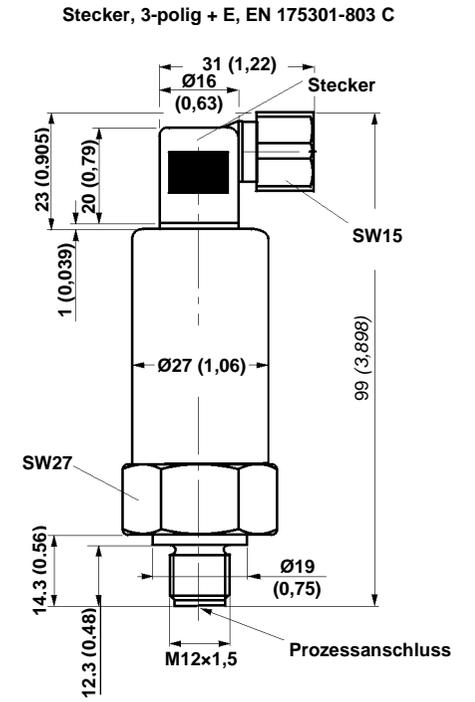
Kolben-/Membran-Druckschalter Typ KLK/KLM-...-S1
